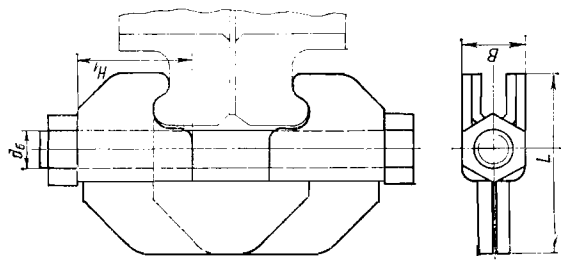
Конструкция стандартного зажима по ОСТ 26-01-385—72
